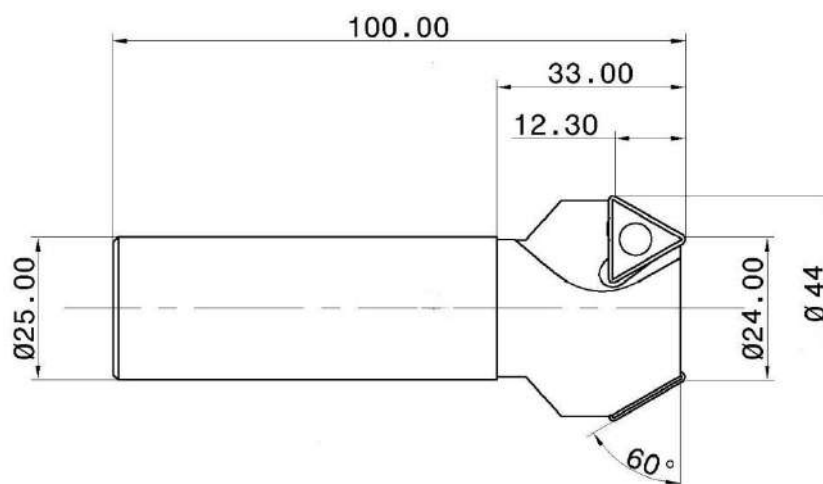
Зенковка ISCAR ED60 D24-W24
